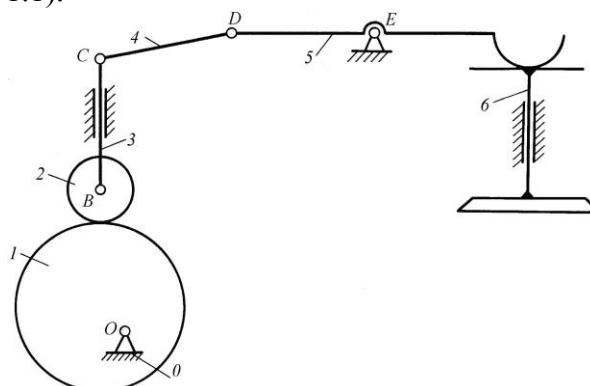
Газораспределительный механизм двигателя вертолёта
